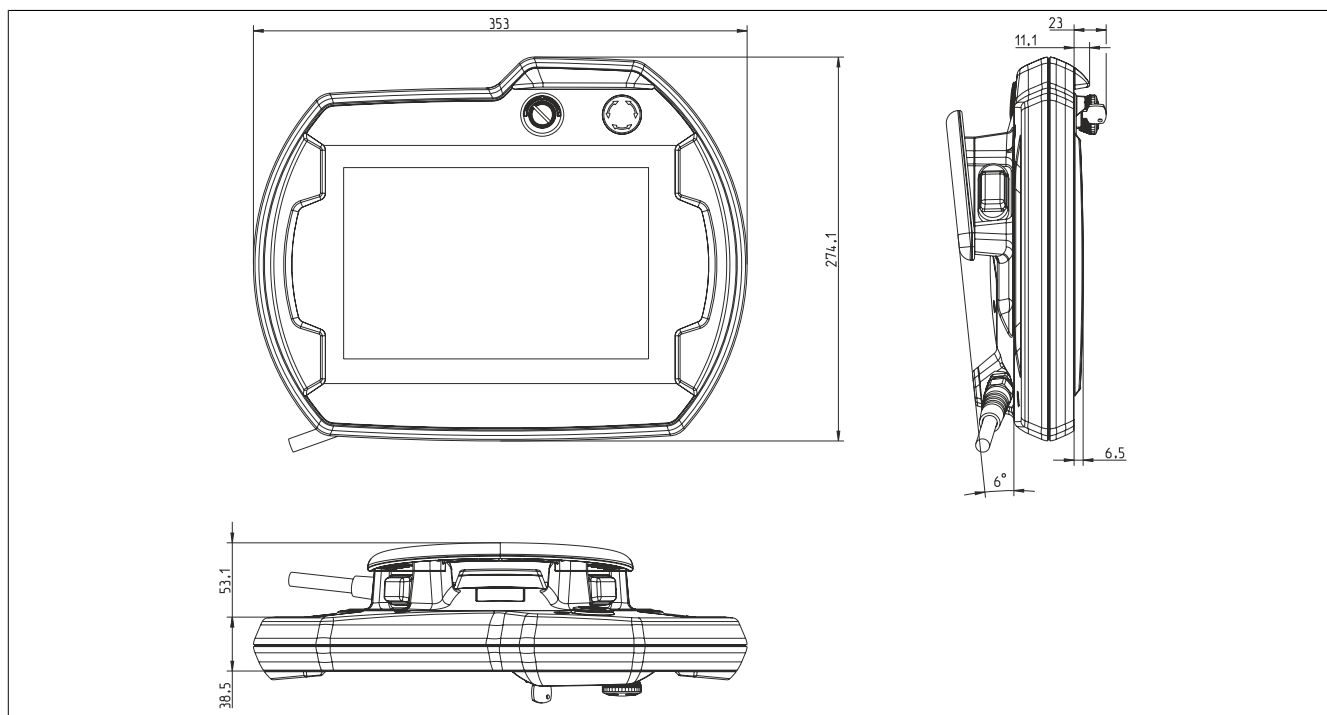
5MP7151.101E-000 - Abmessungen
